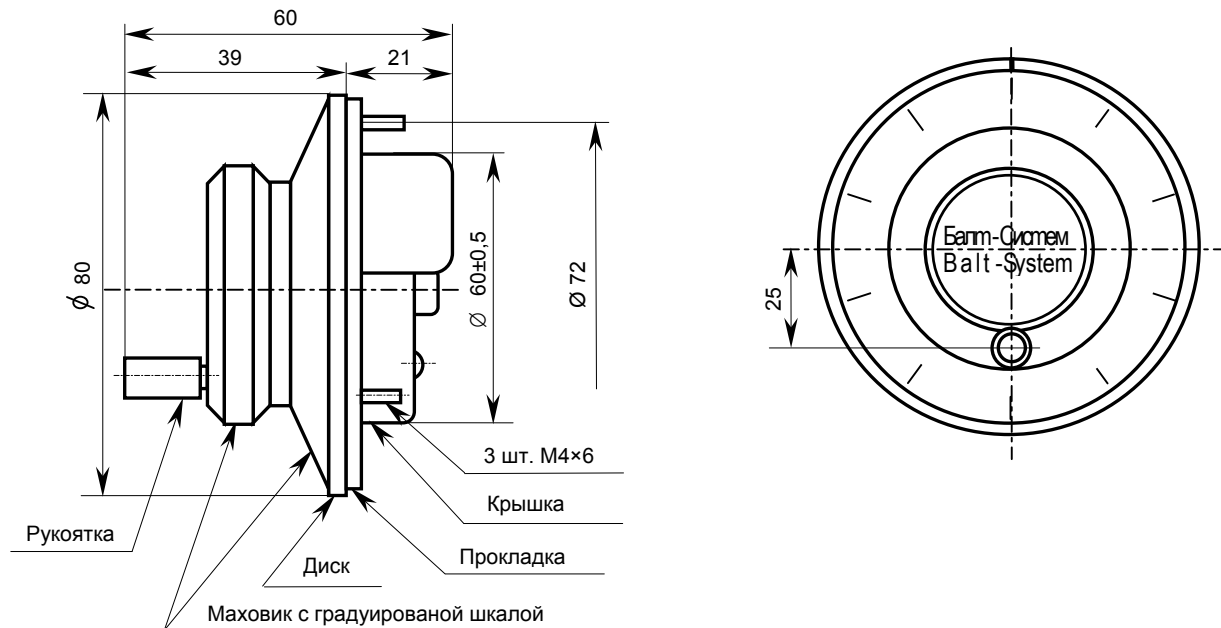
Габаритные размеры штурвала LGF-12-003B-100
